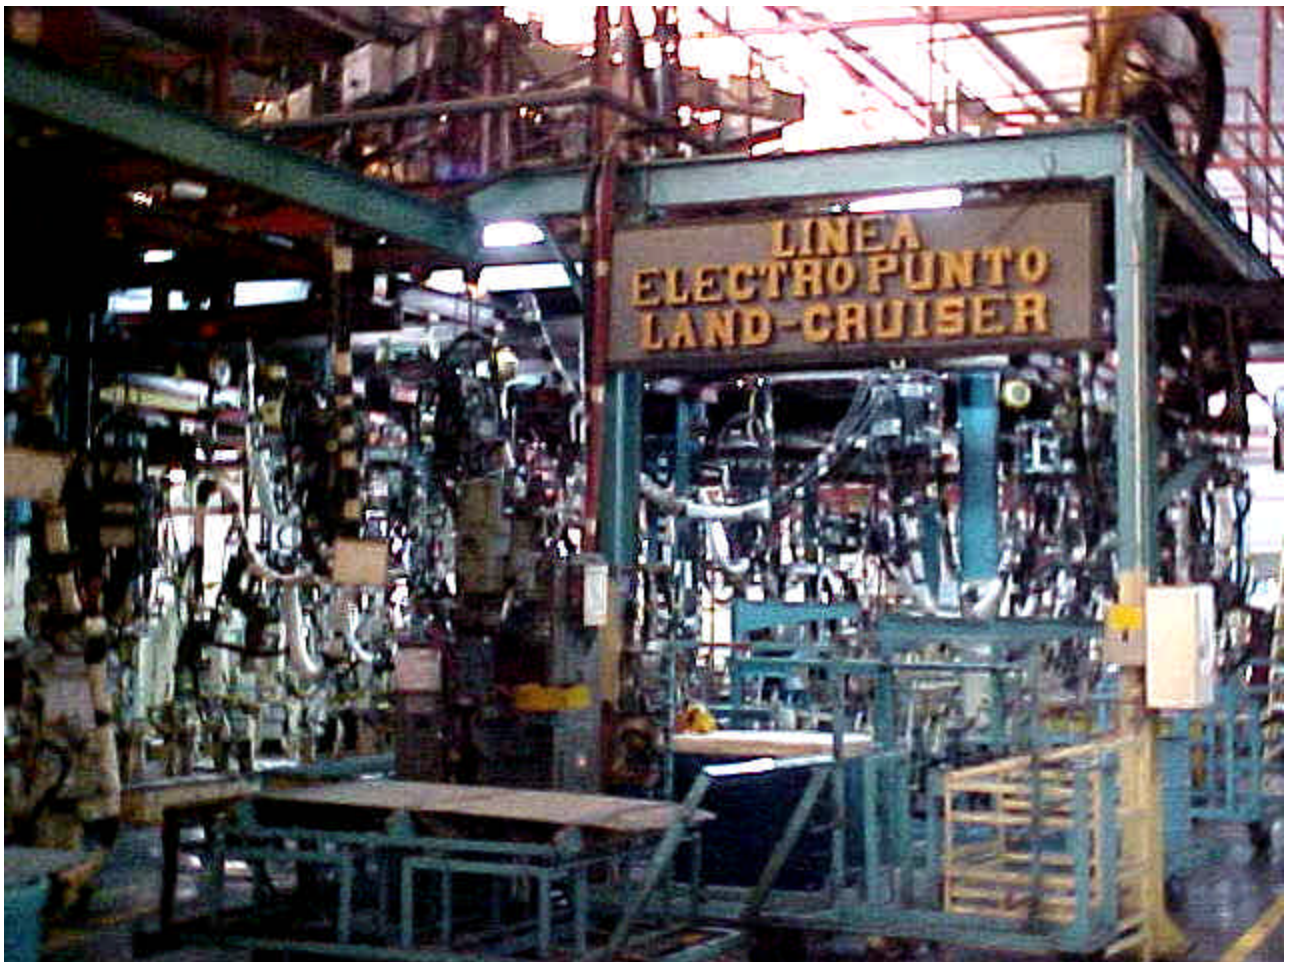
Zona de soldadura por electropunto Land Cruiser
